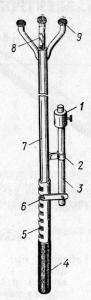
1 — груз; 2 — зажим; 3— рычаг; 4 — ручка; 5 — труба с прорезями; 6 — вилка; 7 — штанга; 8 — трос; 9 — упор
